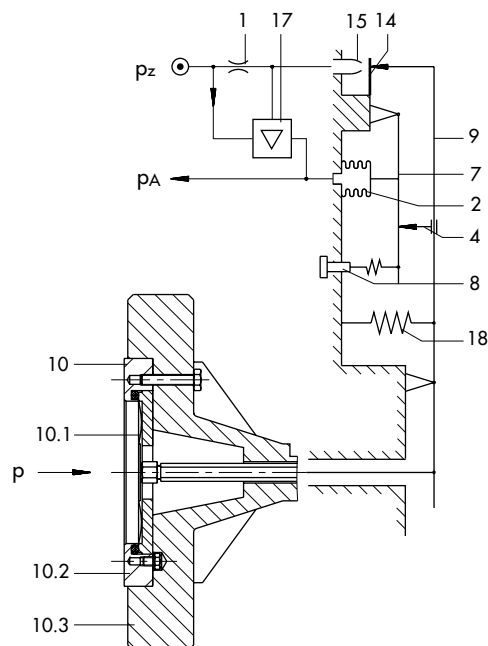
· Pneumatischer Messumformer Typ 814, mit Anschlussflansch PN 10/40, DN 80
